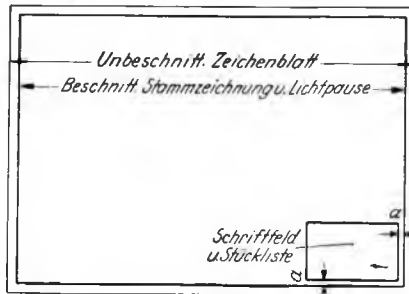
Das unbeschnittene Zeichenblatt, die beschnittene Stammzeichnung und das Schriftfeld.
